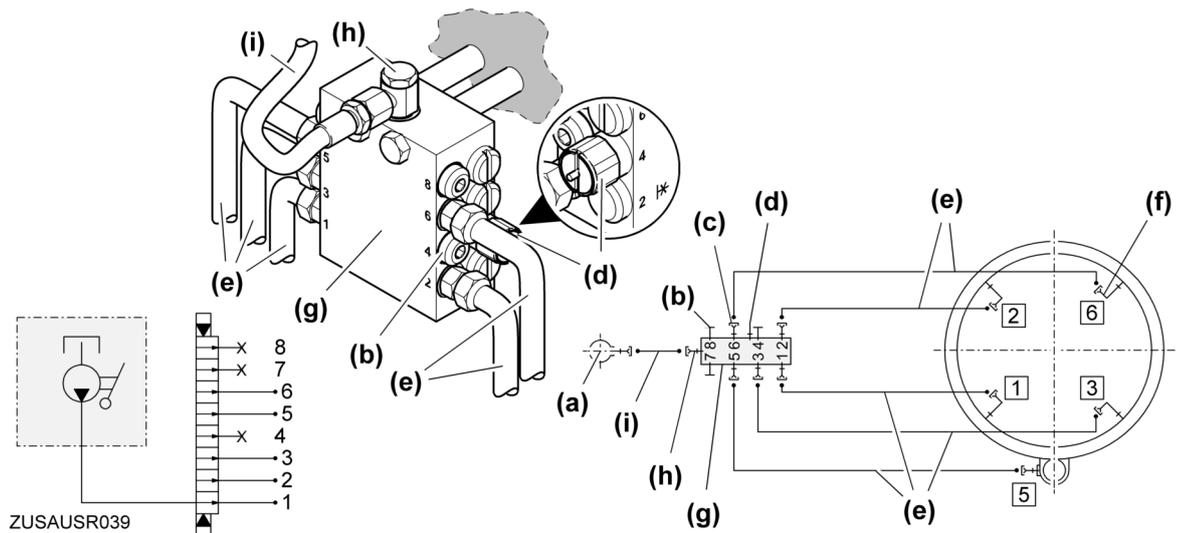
Verlegeplan und Hydraulik-Schaltplan (8er-Verteiler mit 1 Drehwerk)
